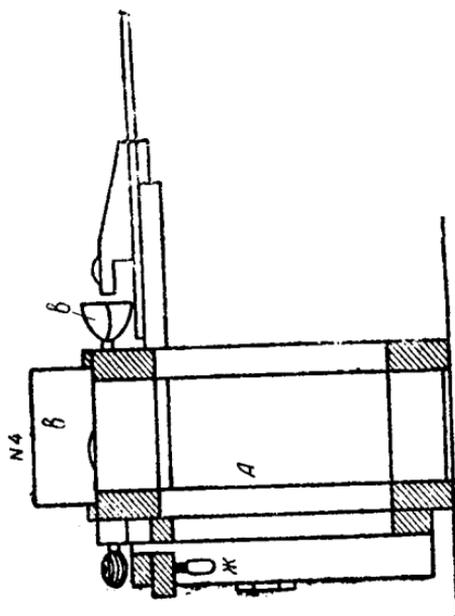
Ложкарный формовочно-фуговальный станок т. Леонова.
